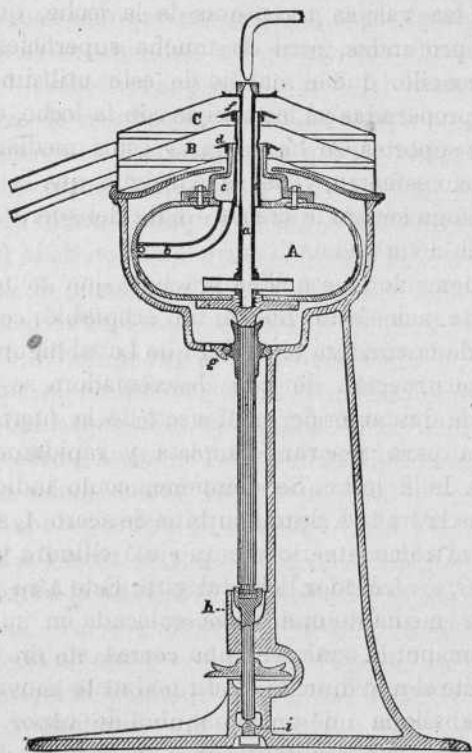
Corte de la descremadora centrifuga de Laval.
